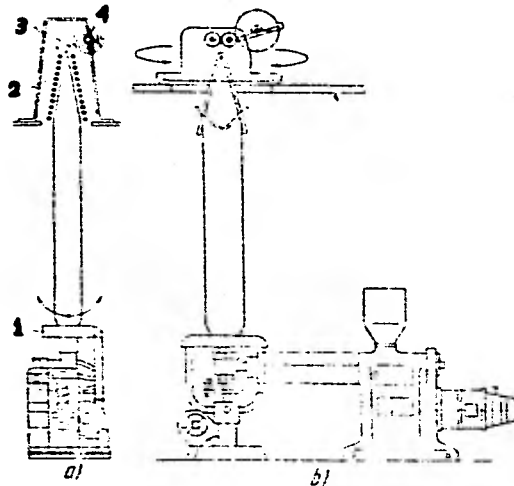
INSTALACION PARA FABRICAR PELICULAS TUBULARES: a). - CON EXTRUSIONADORA OSCILANTE; b). - CON RECOGEDOR OSCILANTE.
